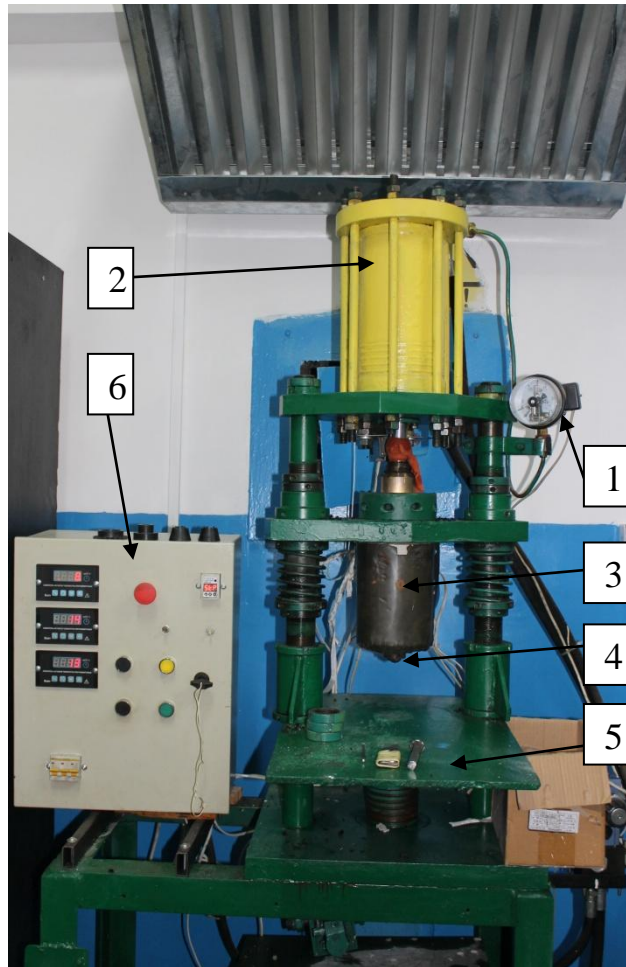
Ливарна машина ручного типу ПЛ-32
